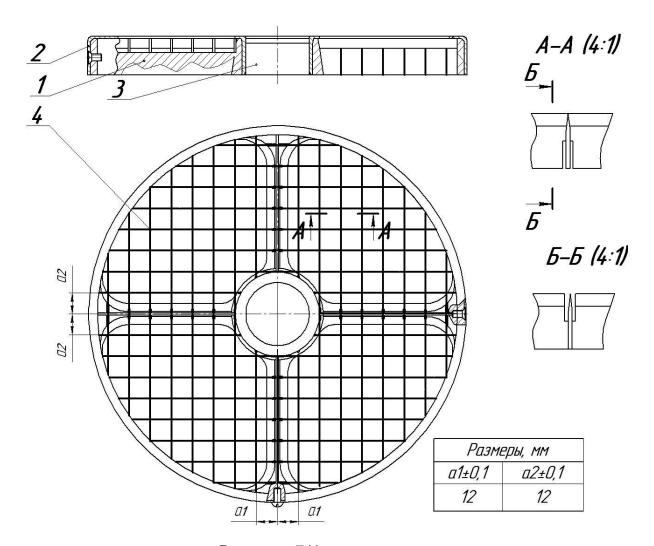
Ножевая решетка: 1 – корпус, 2 – обойма, 3 – втулка, 4 – набор ножей.
